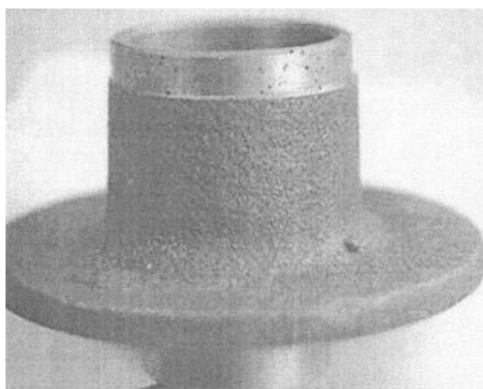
Отливка «Ступица» с гладкими, светлыми раковинами
